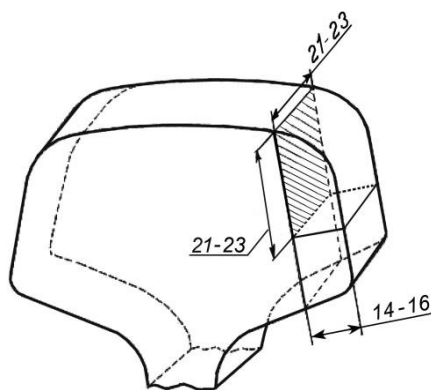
Схема расположения шлифа для контроля неметаллических включений
